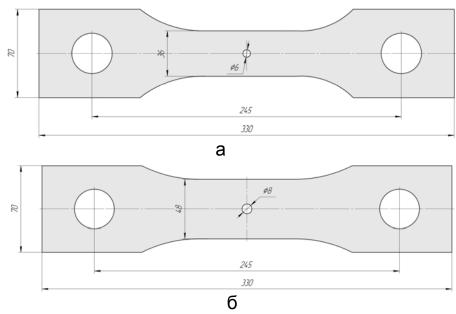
Геометрические параметры образцов: а – из сплава Д16аТ; б – из сплава В95пчТ2
